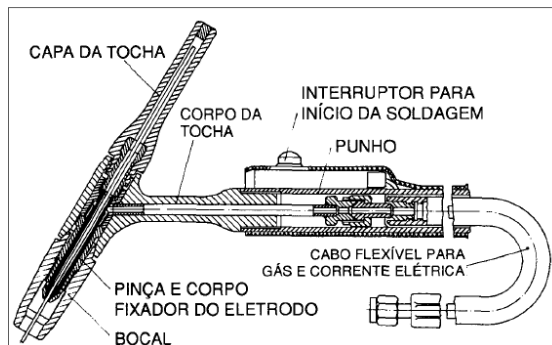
Tocha para soldagem TIG resfriada a ar.
